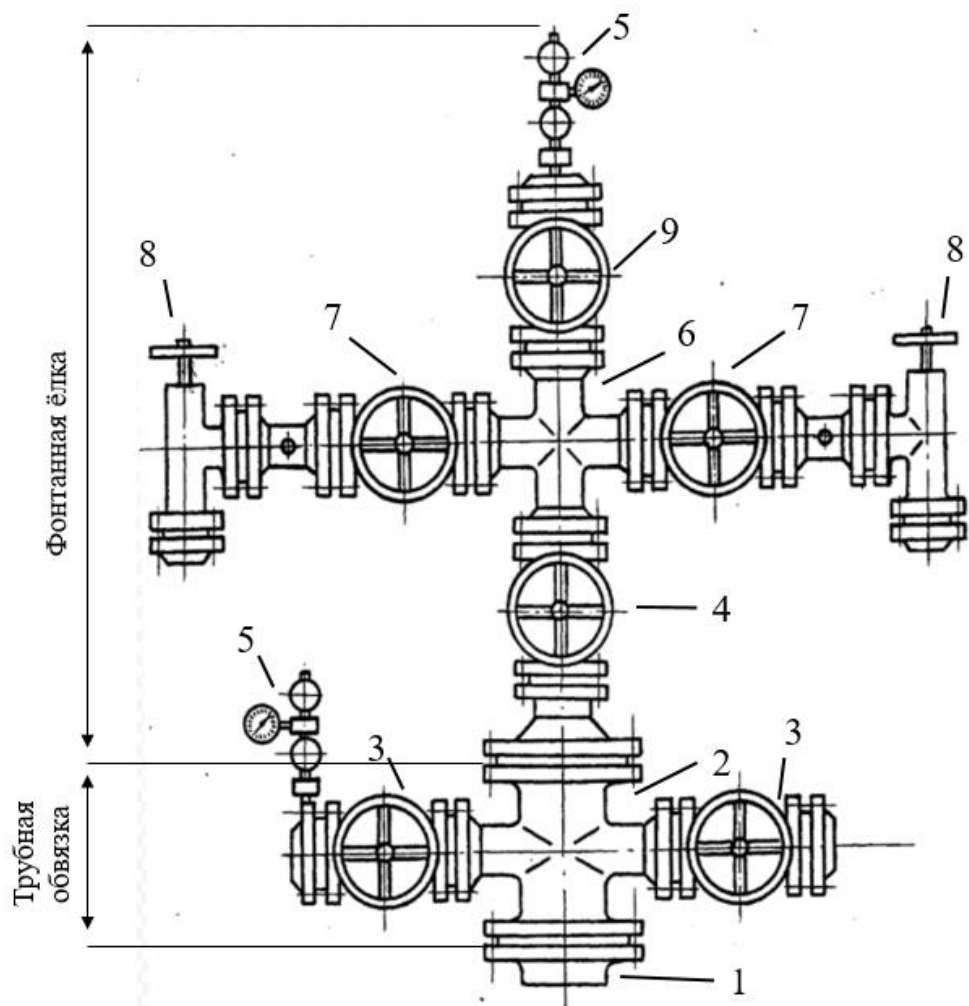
Схема устьевого оборудования газовой скважины:
